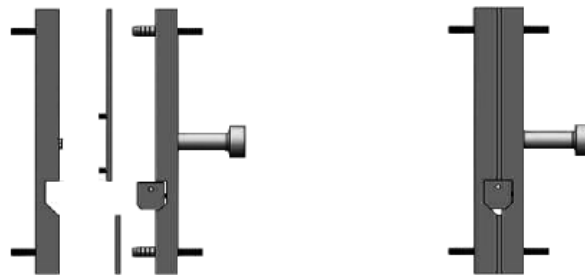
Stampo assemblato aperto (sinistra) e chiuso (destra)
